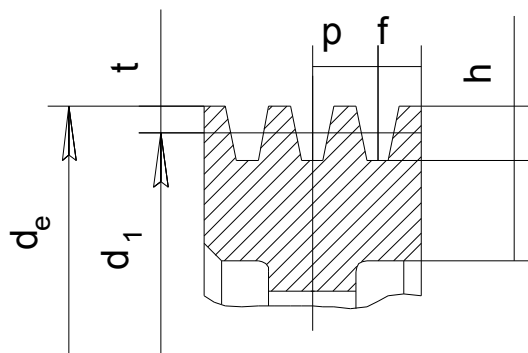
Розрахункова схема поверхні ведучого шківа
